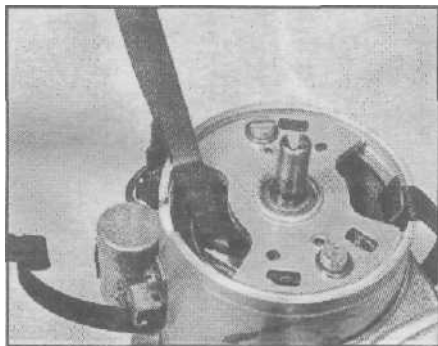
, а. Проверка зазора между контактами прерывателя
